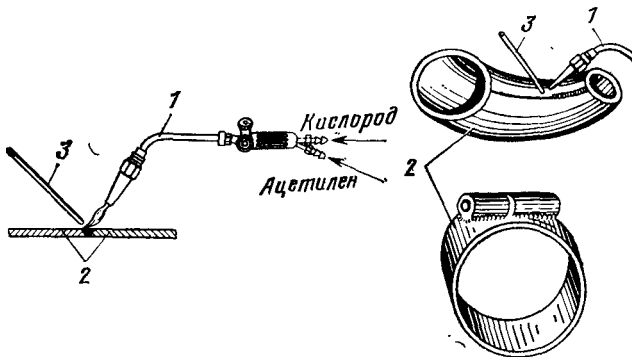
Схема кислородно-ацетиленовой сварки:
